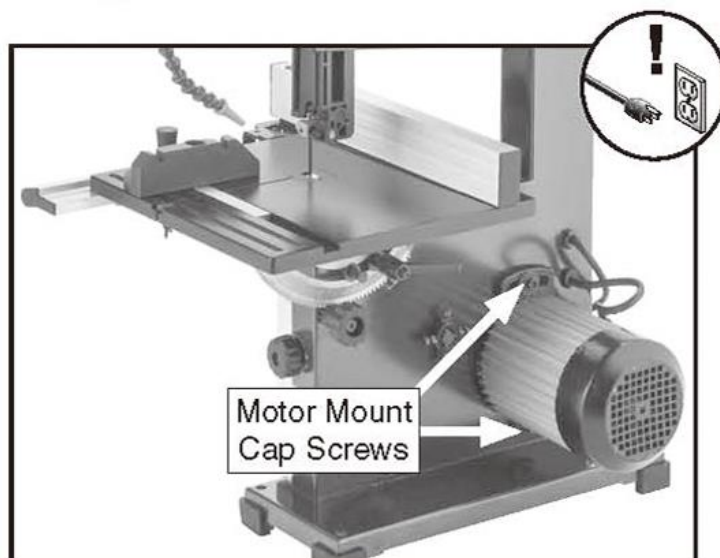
Расположение винтов крепления двигателя, используемых для регулировки натяжения приводного ремня.
